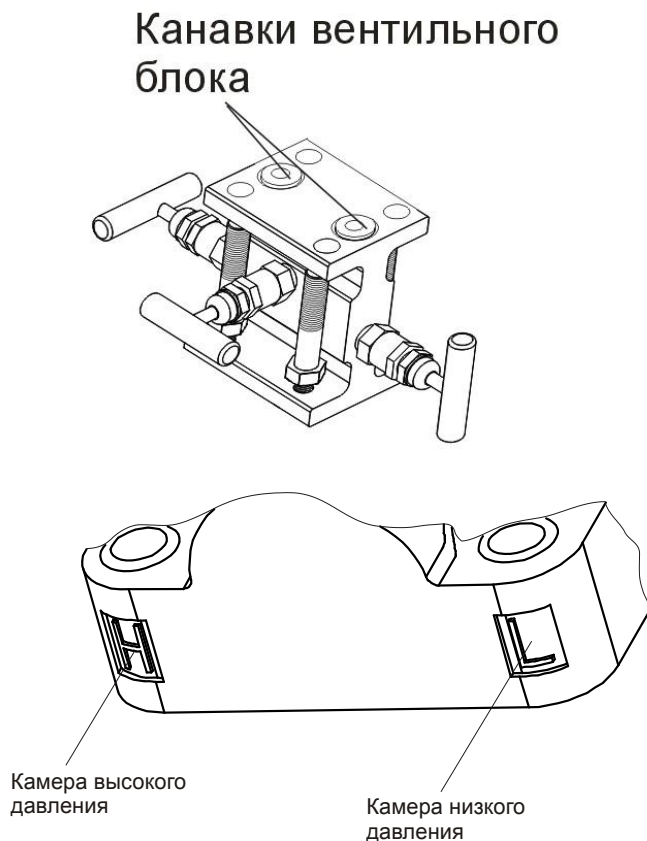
Канавки вентильного блока и маркировка камер высокого и низкого давления на датчике давления (показано без фланца Coplanar)
